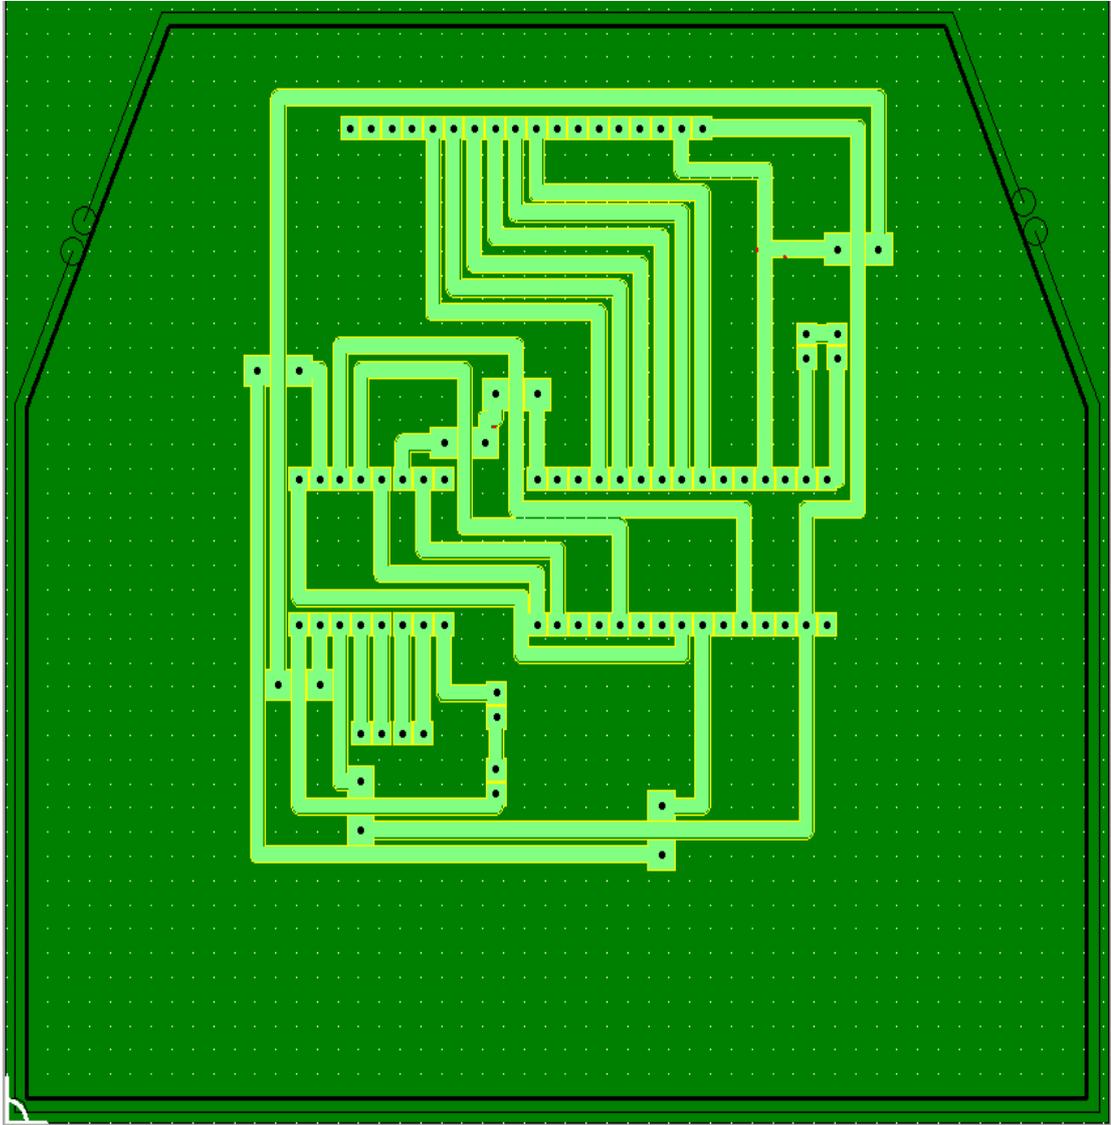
Muestra el número en que el ENGRAVING TOOL pasara diseñando cada pista.
